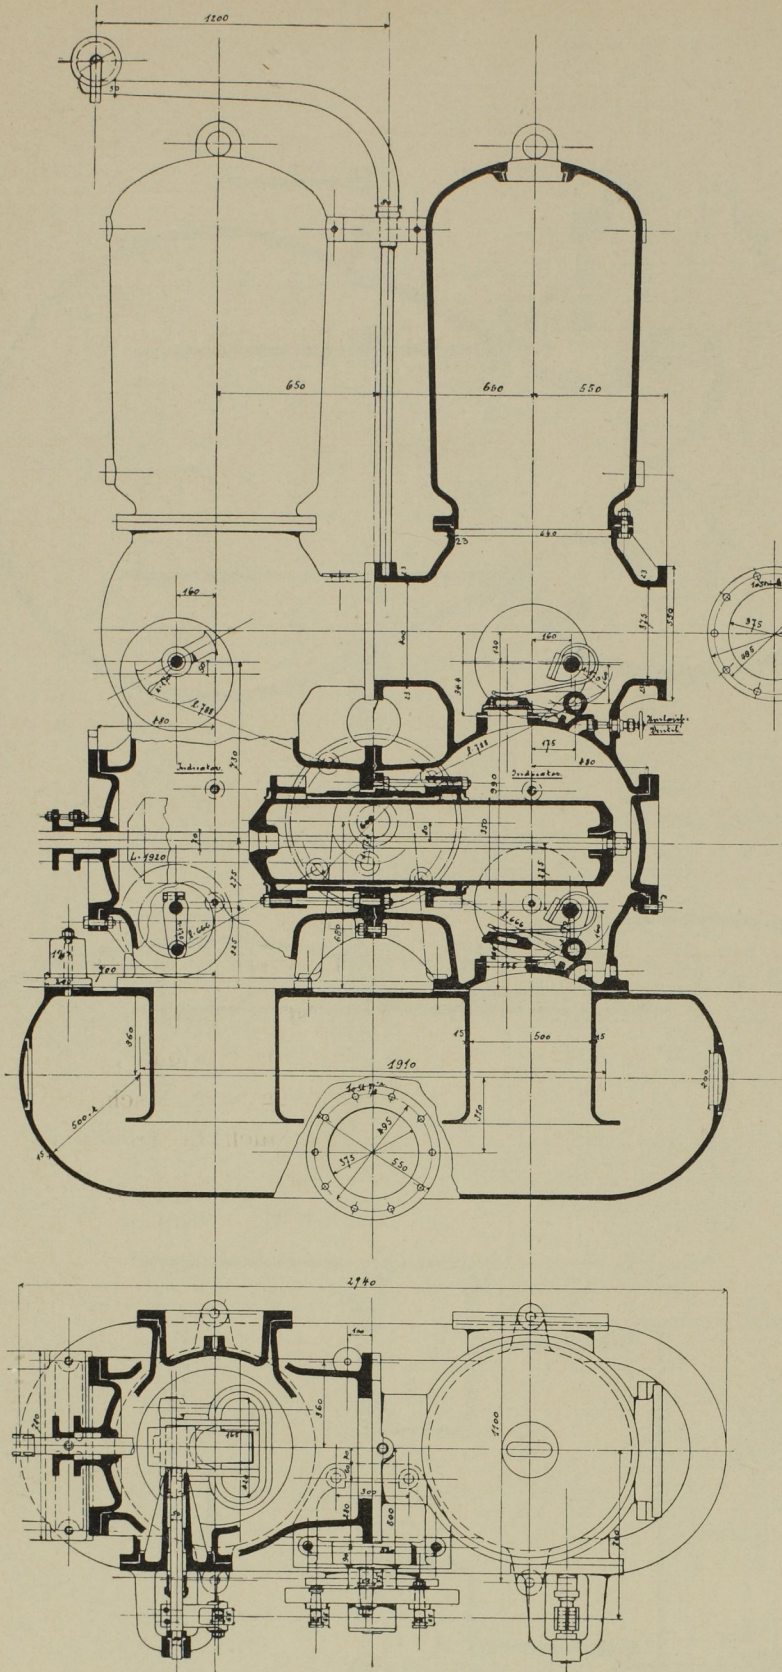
Grundriss der Pumpe. Masst. 1:20.
